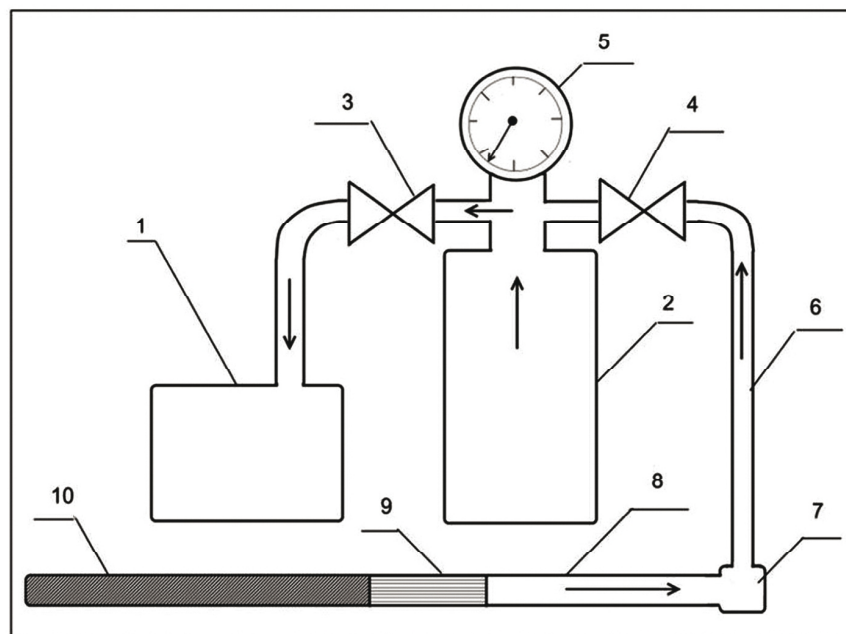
Принципова схема вакуумного пробовідбірника рідкого металу: 1 – вакуумний насос; 2 – ресивер; 3, 4 – вакуумний вентиль; 5 – вакуумметр; 6 – гнучкий герметичний металевий трубопровід; 7 – муфта; 8 – формуювальна кварцова трубка; 9 – охолоджувач; 10 – зразок.
